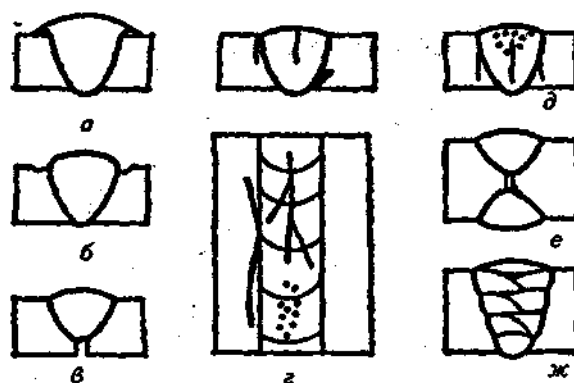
Виды дефектов в сварных соединениях: а — наплыв; б — подрез; в — непровар; г — наружные трещины и поры; д — внутренние трещины и поры; е — внутренний непровар; ж — шлаковые включения
